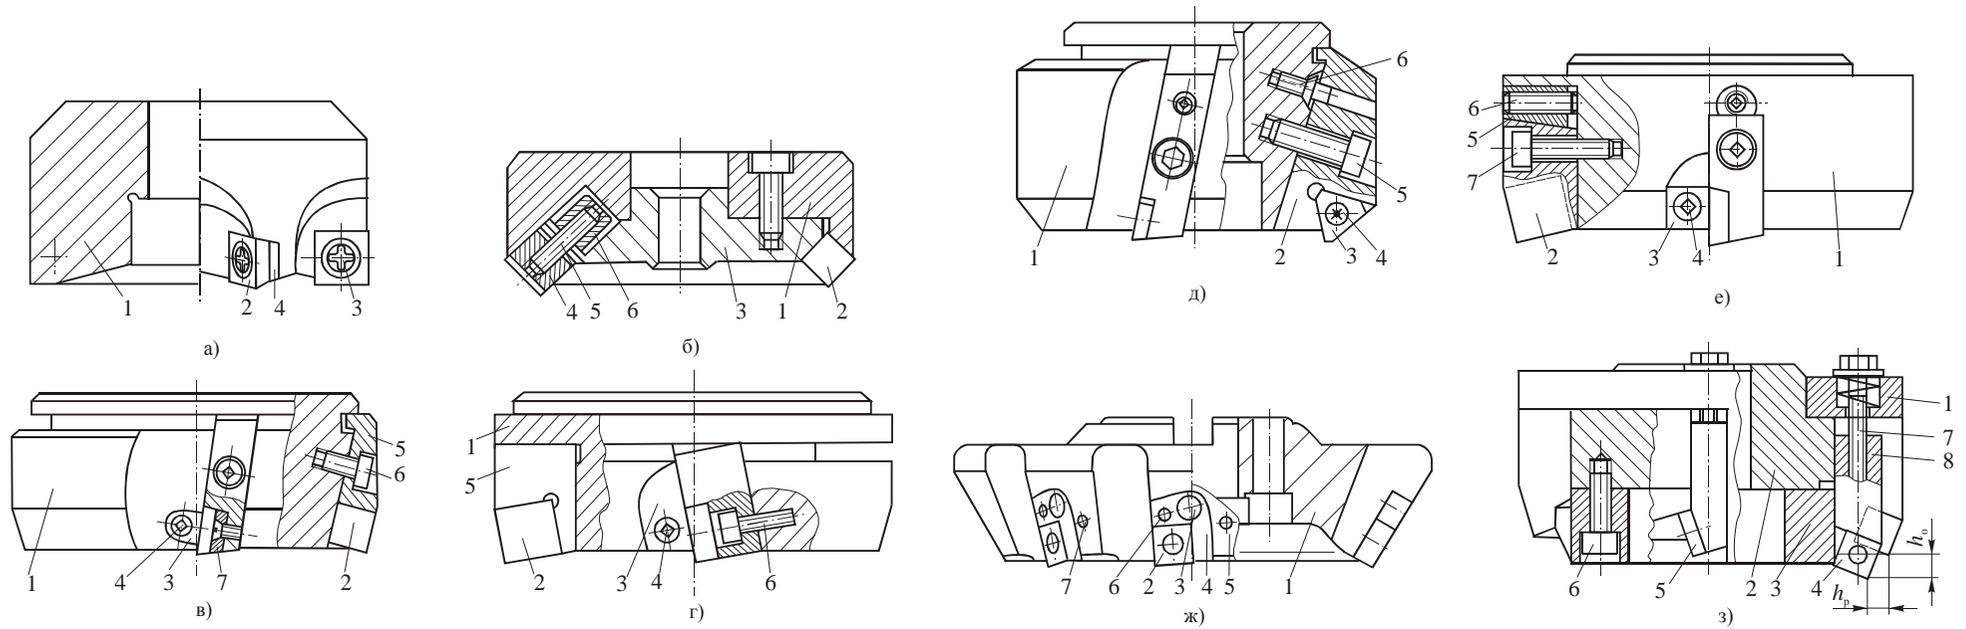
Торцевые фрезы, оснащенные СМП: *а* – базы под пластины в корпусе фрезы; *б* – базы под пластины на составных частях корпуса; *в* – с вкладышами и двумя базами; *г* – с вкладышами (кассетами) и тремя базами во вкладышах; *д* – с вкладышами, регулируемые винтом; *е* – с вкладышами, регулируемые клином; *ж* – с тангенциальным креплением пластин; *з* – со ступенчатым расположением пластин
